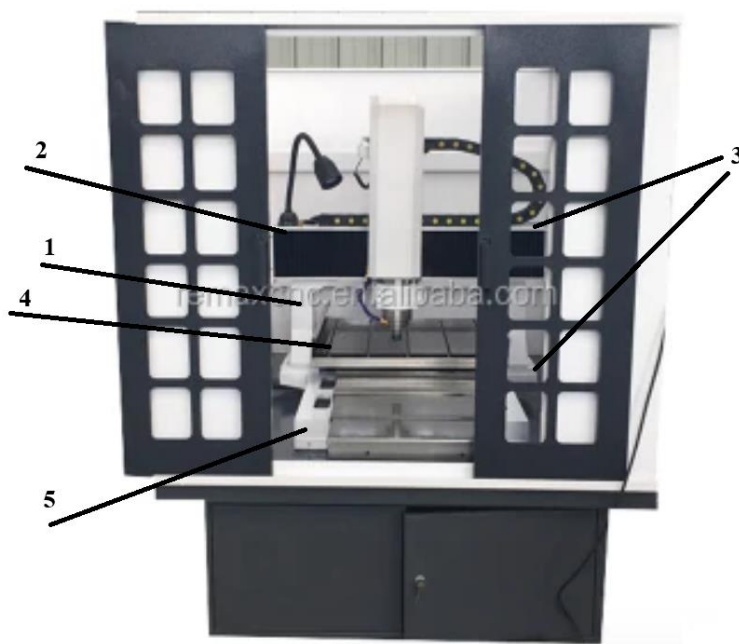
Загальний вигляд верстата для виготовлення прес-форм з ЧПУ: 1 – опори, 2 – шагові двигуни, 3 – лінійні напрямні, 4 – робоча поверхня, 5 – станина [45]
